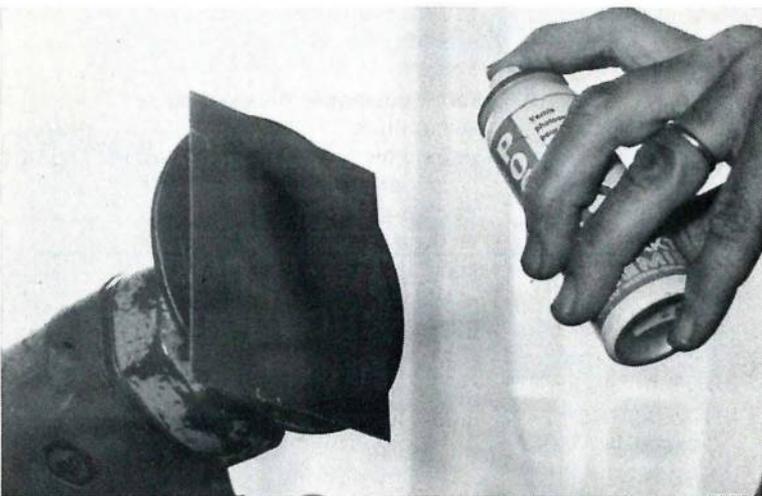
Pulvérisation de la résine sur la plaquette en rotation
